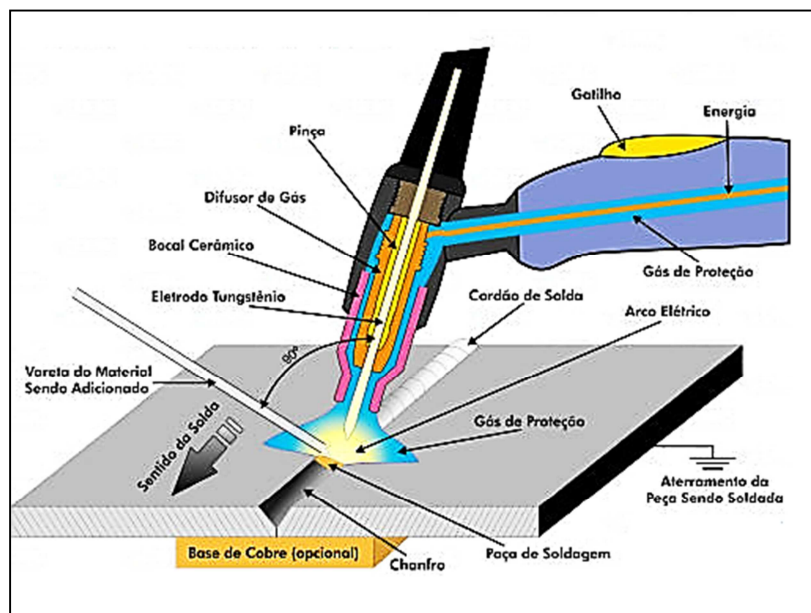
Processo de soldagem GTAW ou TIG (Adaptado de DBC guias tutorias, processos de soldagem).
